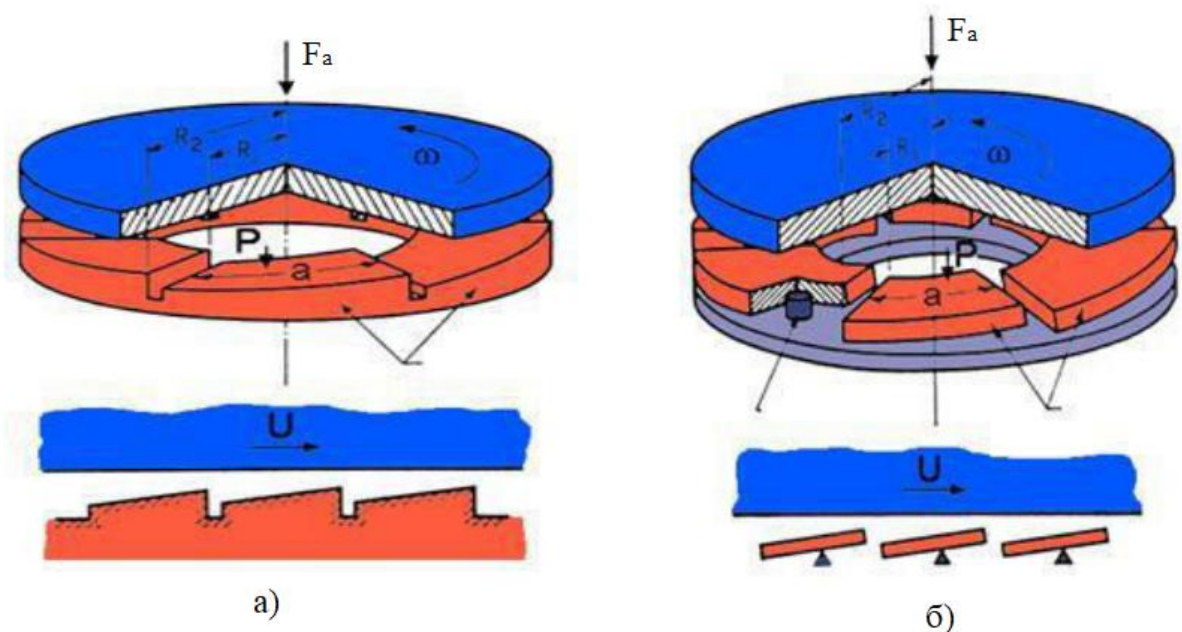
Упорний підшипник ковзання з: а – фіксованим нахилом колодок, б – самовстановлювальними колодками
